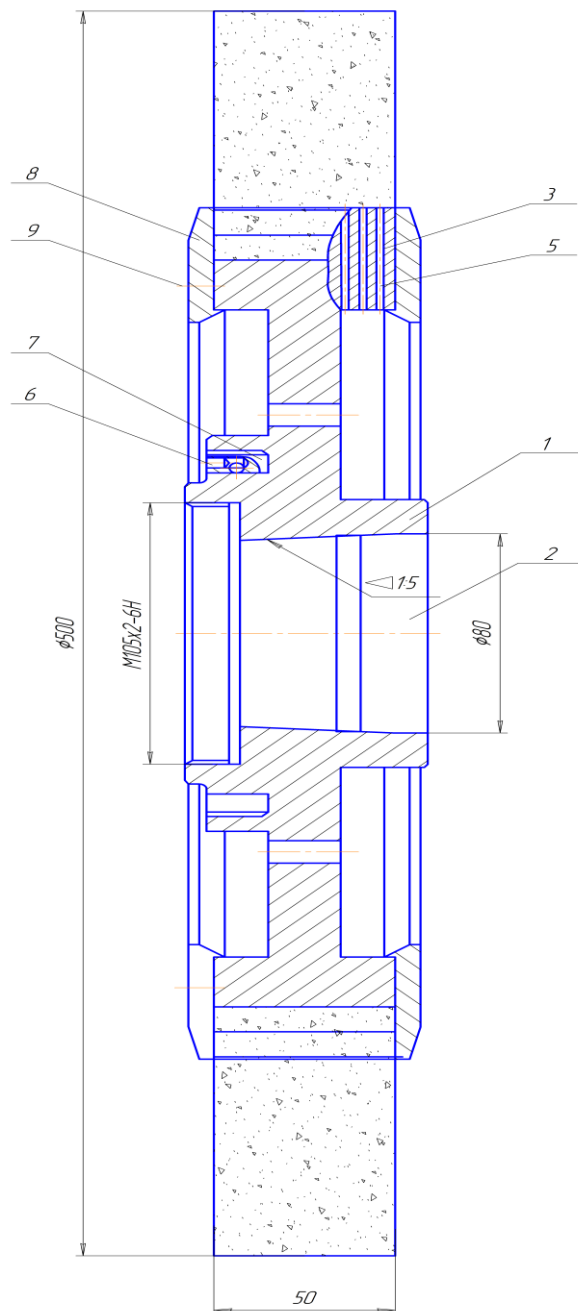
Сечение дискретного абразивного инструмента сборной конструкции, приведенной на рис. 5.3.
